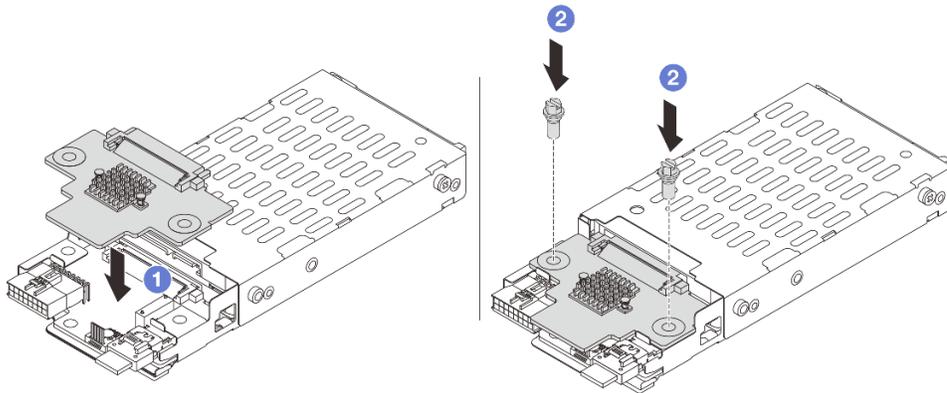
Installation d'un fond de panier d'unité 7 mm (haut)
